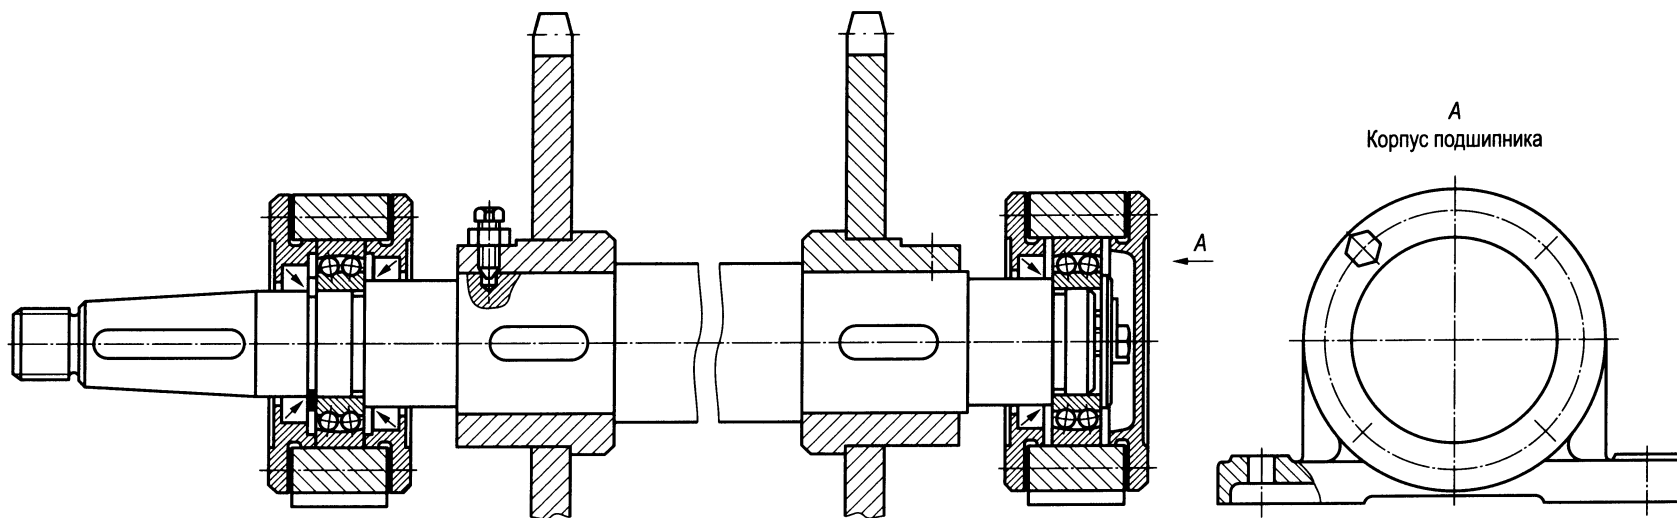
Вал приводной со сварными звездочками
